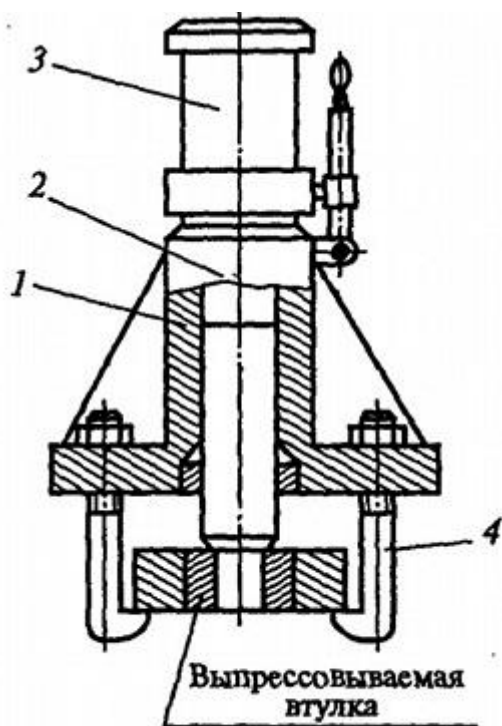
Гидравлический съемник: 1 – цилиндр; 2 – поршень; 3 – плунжерный насос; 4 – захват
